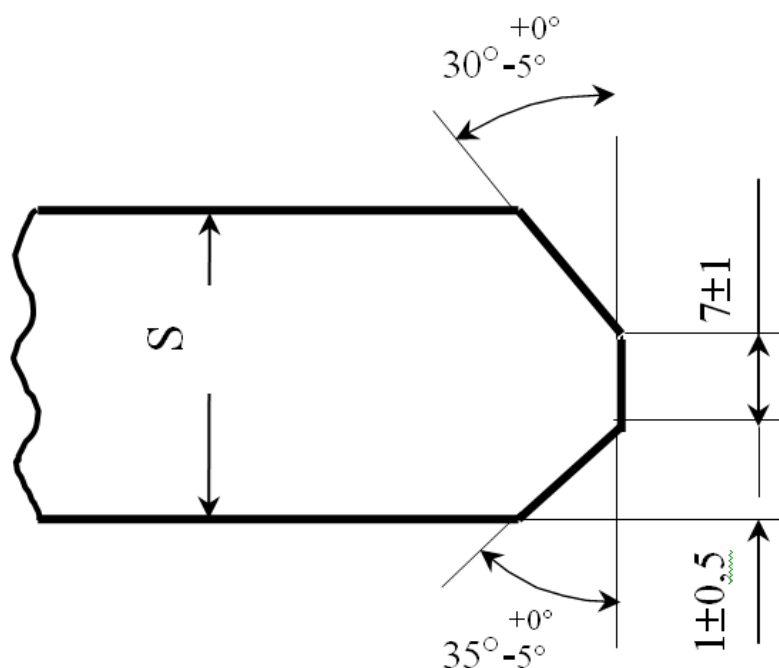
Форма разделки кромок при сварке под флюсом
